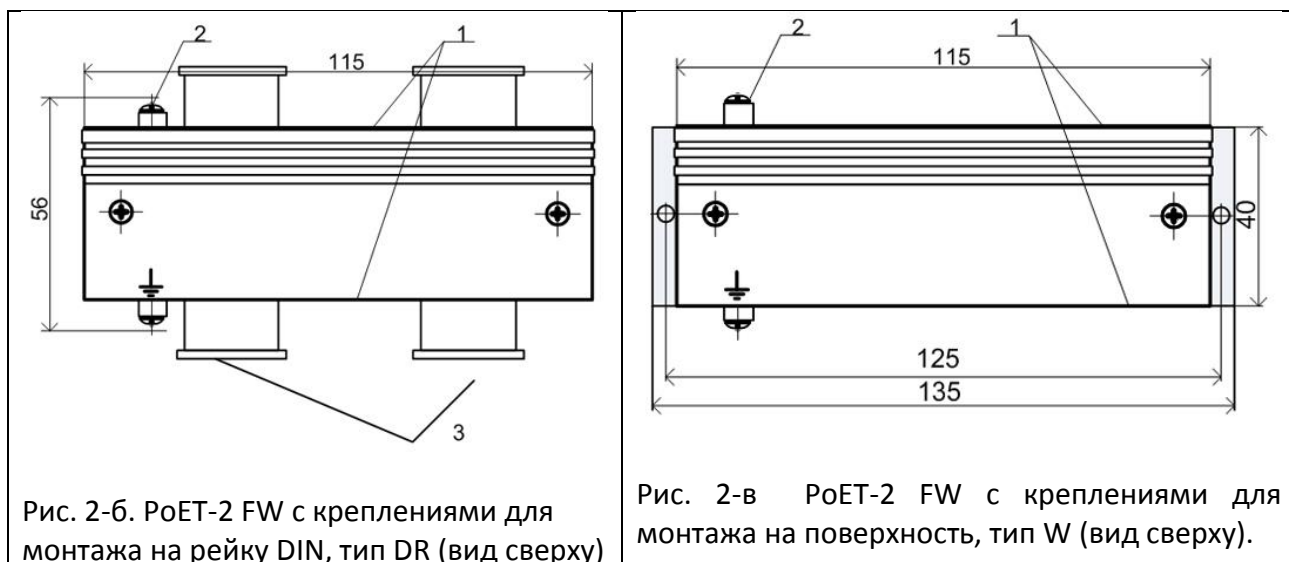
б. PoET-2 FW с креплениями для монтажа на рейку DIN, тип DR (вид сверху)
